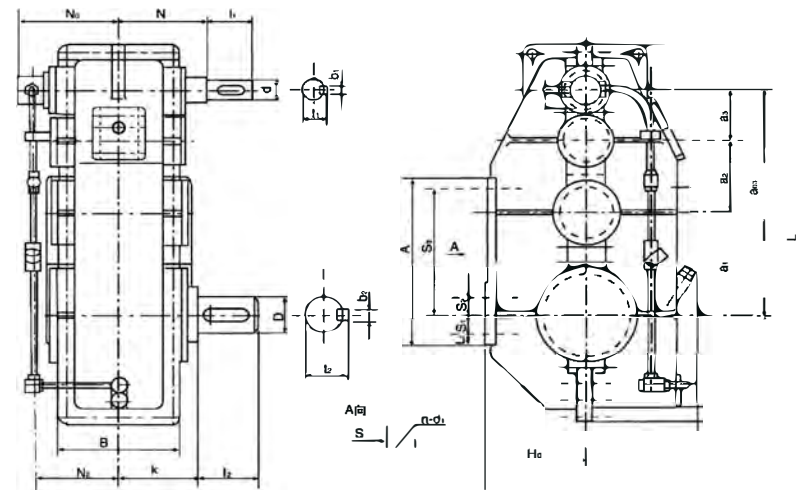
, Габаритные и установочные размеры редуктора QJ-L
